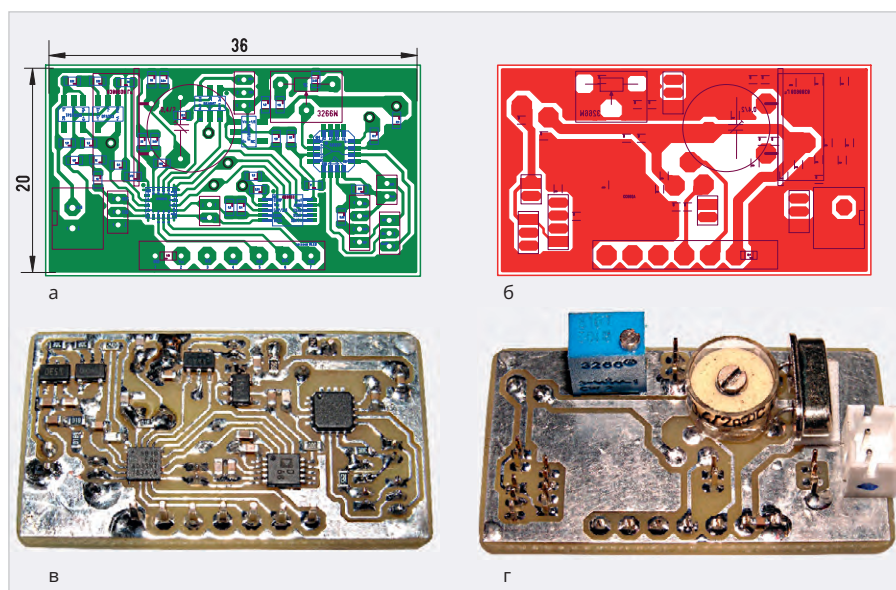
Разводка и внешний вид платы прибора: а, в – вид со стороны расположения SMD-компонентов; б, г – вид с обратной стороны
